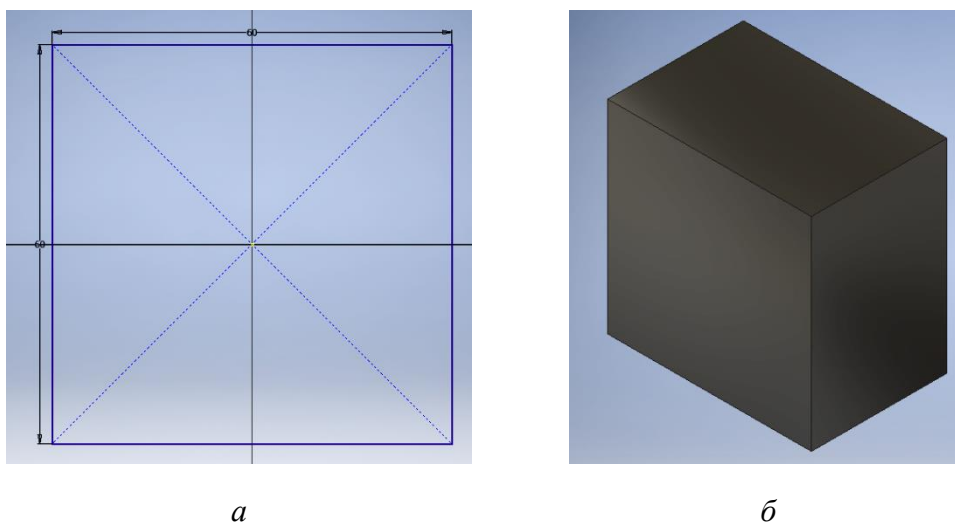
Эскиз (а) и 3D-модель (б) корпуса
